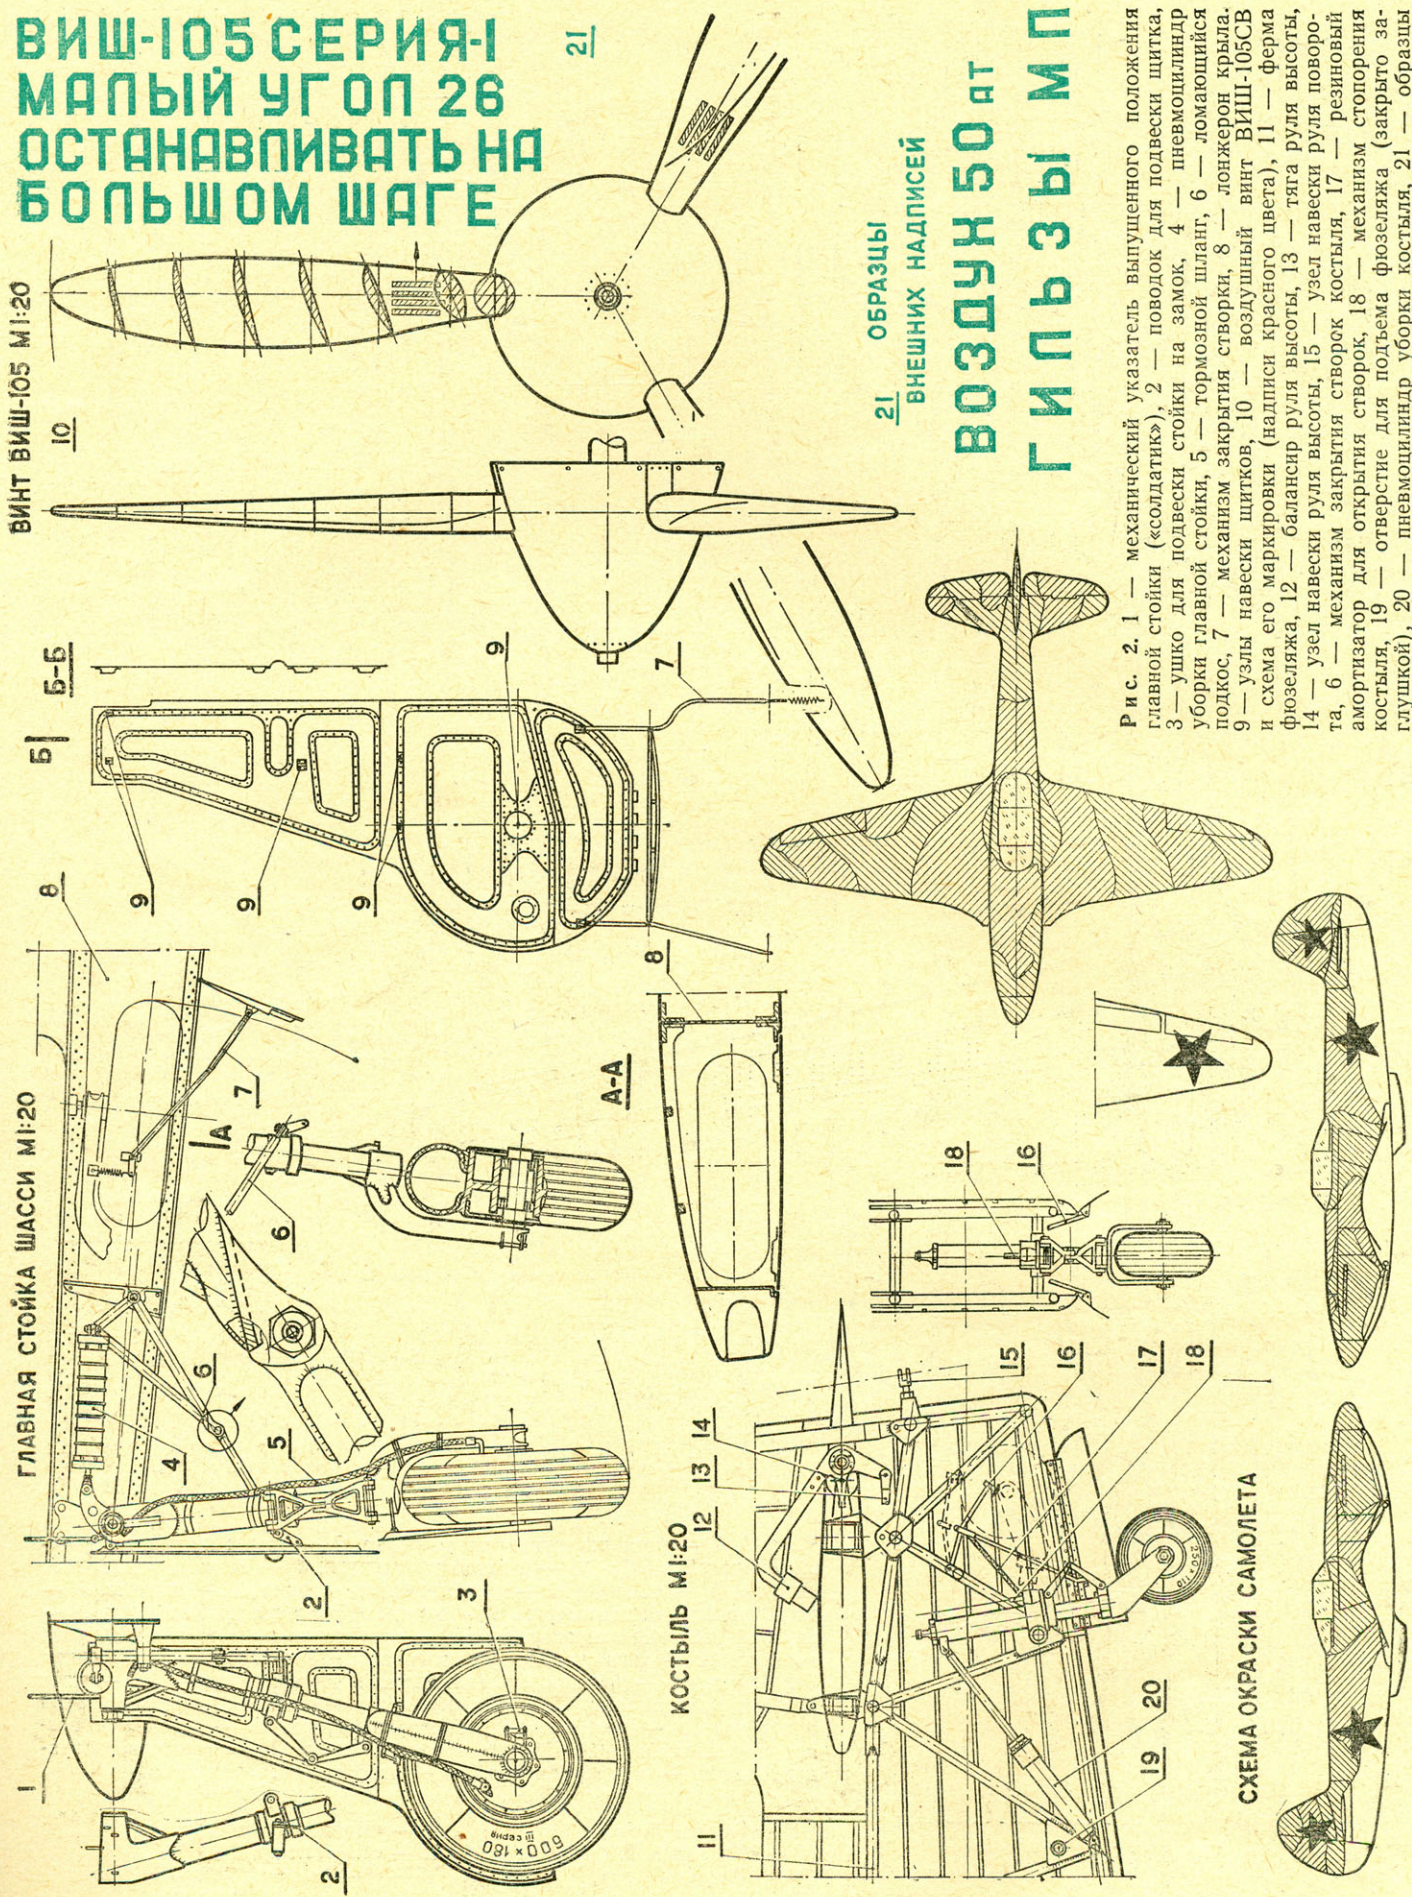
1 — механический указатель выпущенного положения главной стойки («солдатык»), 2 — поводок для подвески щитка, 3 — ушко для подвески стойки на замок, 4 — пневмоцилиндр уборки главной стойки, 5 — тормозной шланг, 6 — ломающийся подкос, 7 — механизм закрытия створки, 8 — лонжерон крыла, 9 — узлы навески щитков, 10 — воздушный винт ВИШ-105СВ и схема его маркировки (надписи красного цвета), 11 — ферма фюзеляжа, 12 — балансир руля высоты, 13 — тяга руля высоты, 14 — узел навески руля высоты, 15 — узел навески руля поворота, 16 — механизм закрытия створок костыля, 17 — резиновый амортизатор для открытия створок, 18 — механизм стопорения костыля, 19 — отверстие для подъема фюзеляжа (закрыто заглушкой), 20 — пневмоцилиндр уборки костыля, 21 — образцы внешних надписей (надписи красного цвета, высота букв 20 мм).
